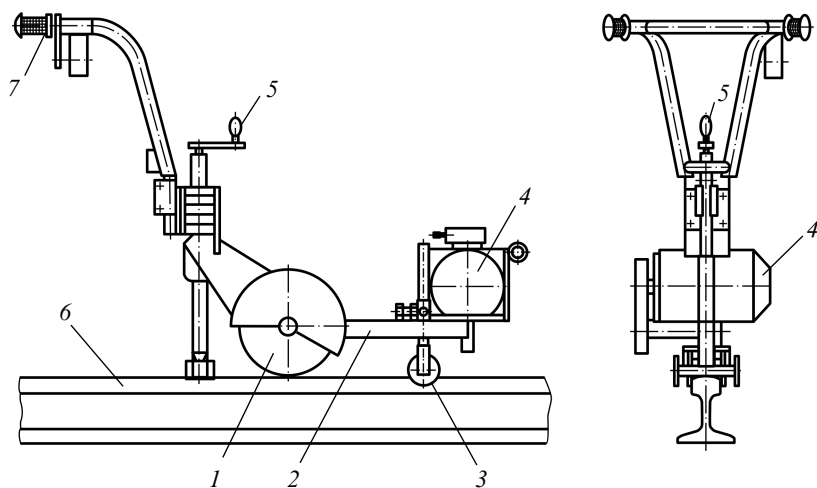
Станок для шлифовки наплавленных концов рельсов:
